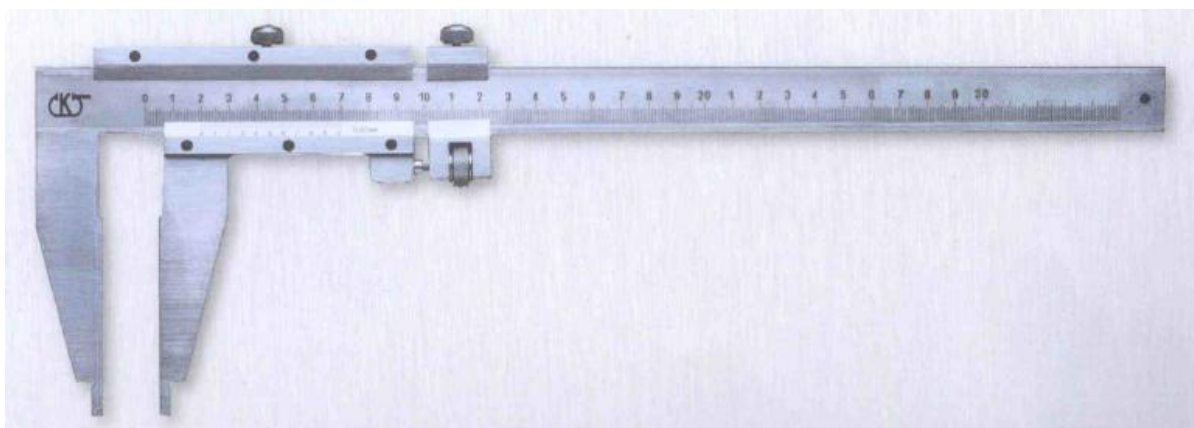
Общий вид штангенциркулей ШЦ-III.
